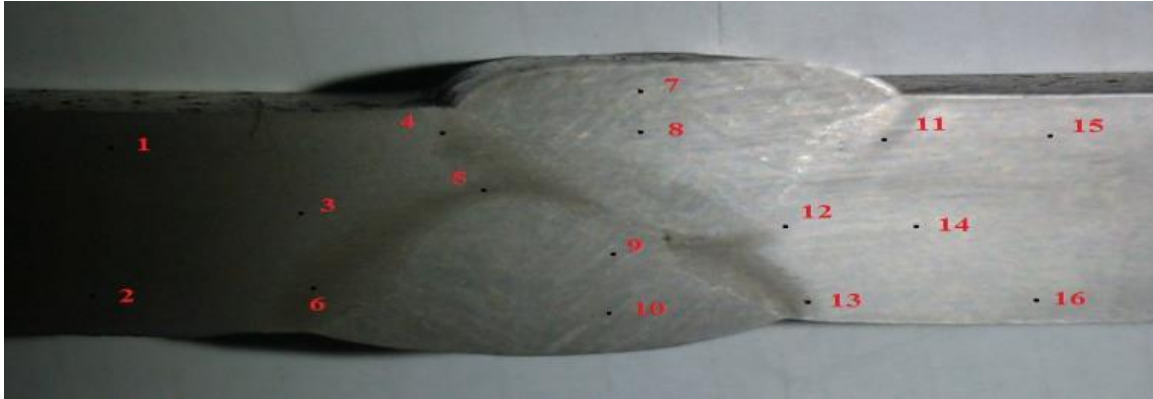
Éprouvettes avec joint de soudure bout à bout pour la dureté Vickers (Acier X 60M)
